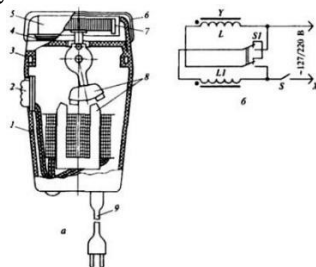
Электробритва «Микма-101»: а) конструкция: 1 – корпус; 2 – выключатель; 3 – кожух; 4 – устройство для стрижки; 5 – неподвижный нож; 6 – защитный колпачок; 7 – подвижный нож; 8 – электромагнитный вибратор; 9 – соединительный шнур; б) электрическая схема: Y – статор; L, L1 – катушки статора; S1 – переключатель; S – выключатель; X – штепсельный разъем
